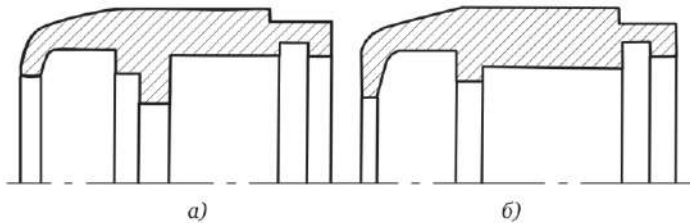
Приклад конструктивних виконань кришки підшипника редуктора, оброблених за дві (а) і одну (б) установки
